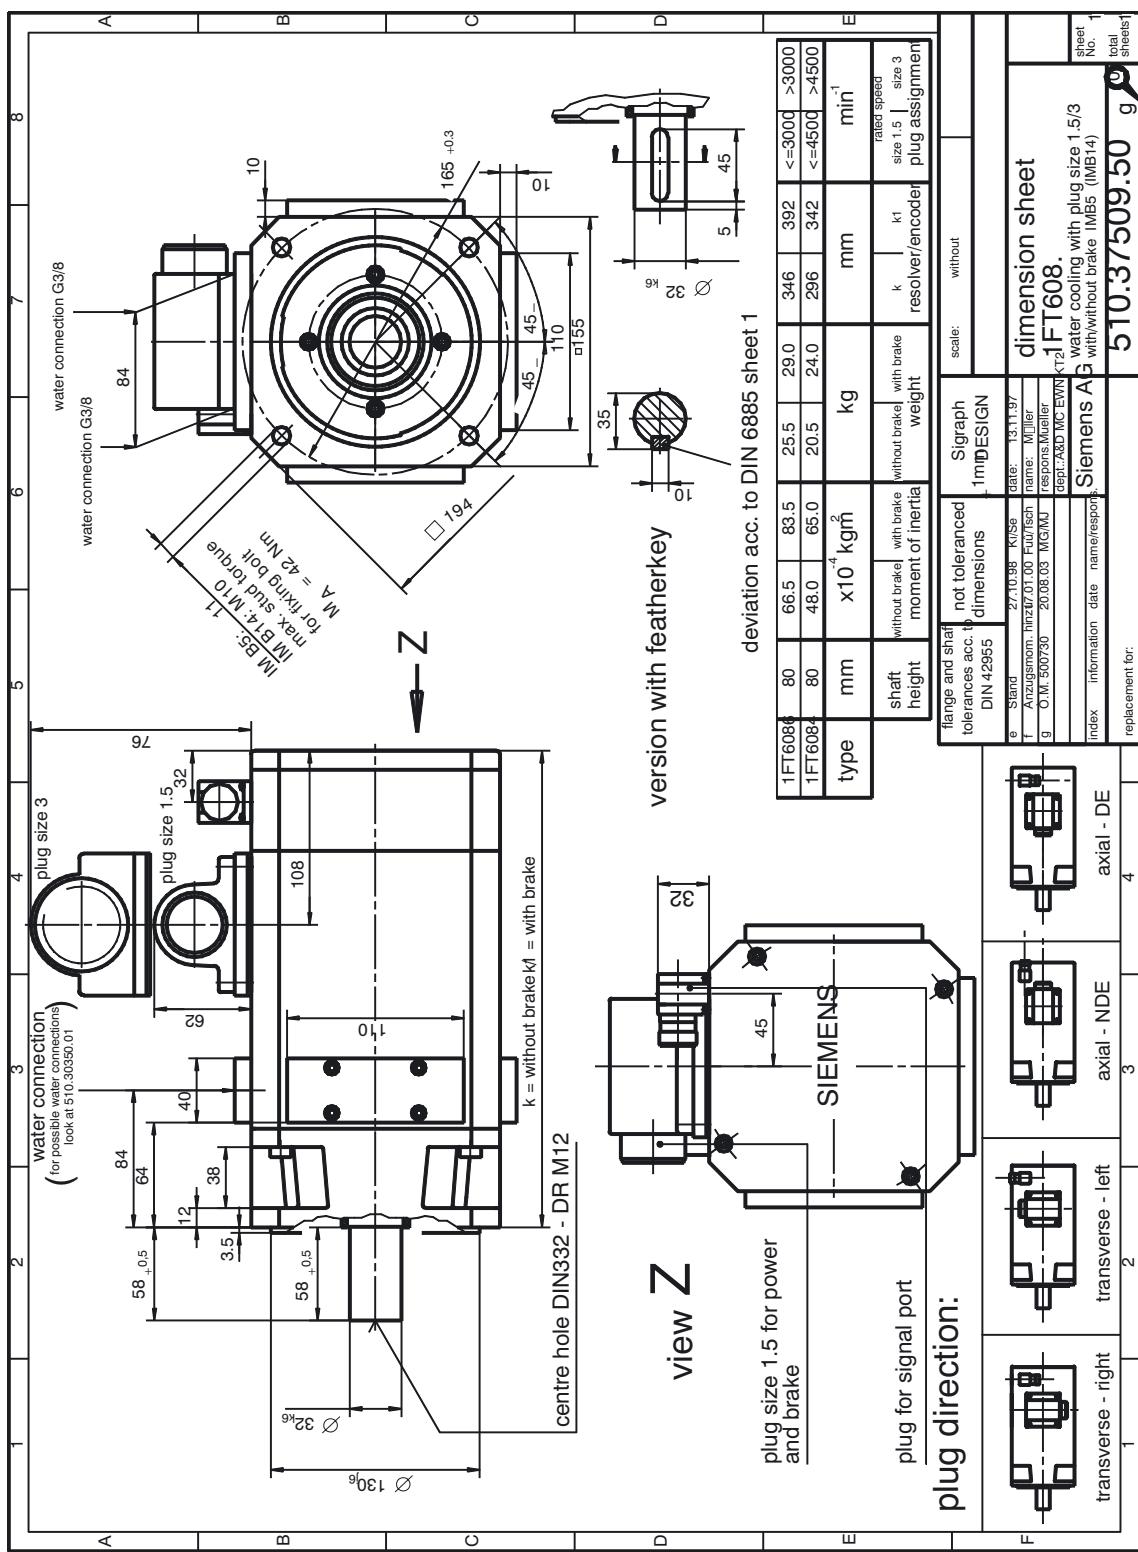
1FT608□ wassergekühlt mit Stecker Größe 1.5/3
